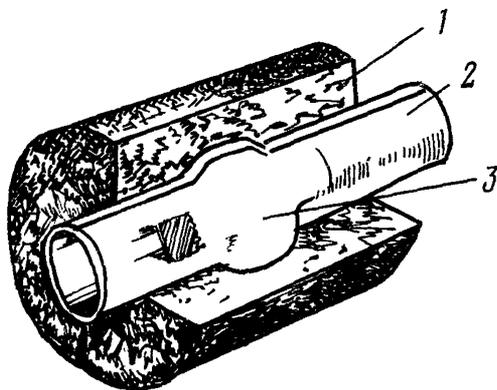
Термитный патрон марки АС для сварки жил проводов и кабелей:
